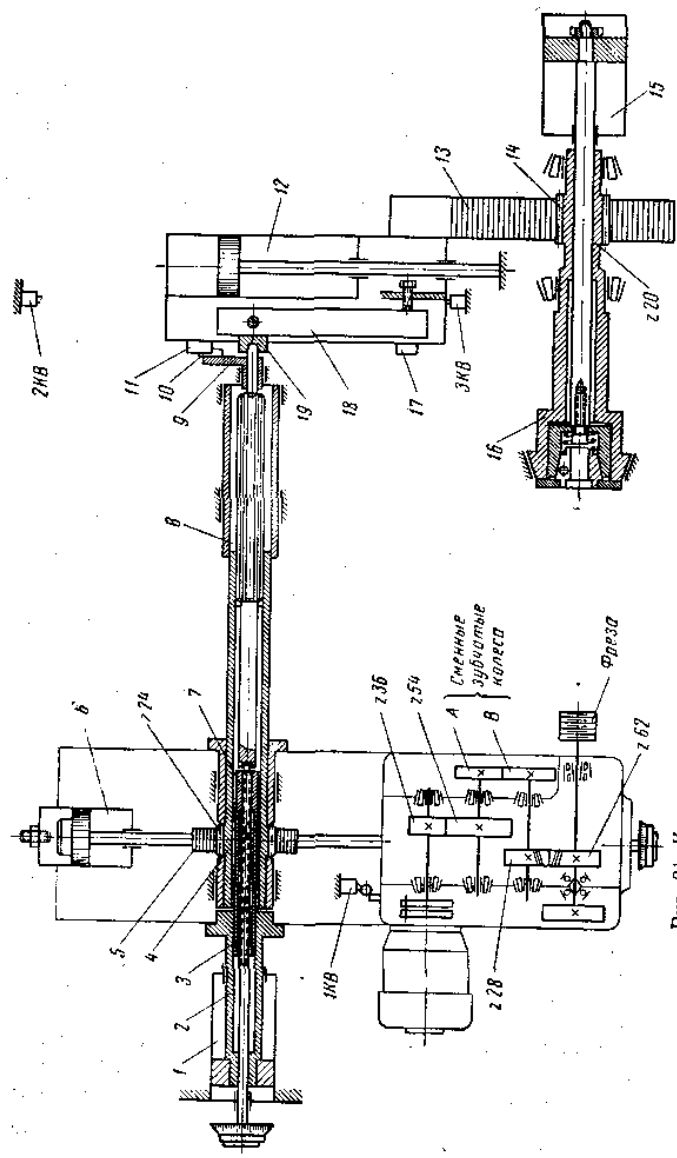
Кинематическая схема резьбофрезерного полуавтомата КТ86
